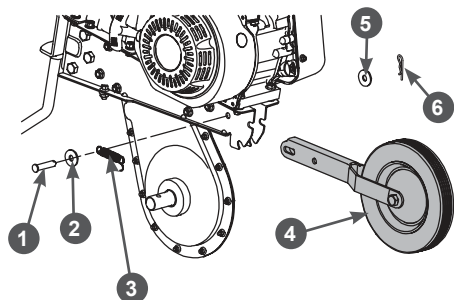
Установка транспортировочного колеса (внутренний палец)
